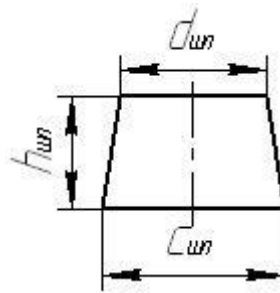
Схематичне зображення перерізу шлаковловлювача
